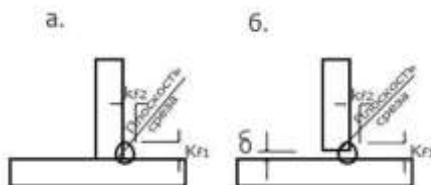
Сечения сварных швов в образцах, испытанных на сдвиг без зазора (а) и с зазором (б)
